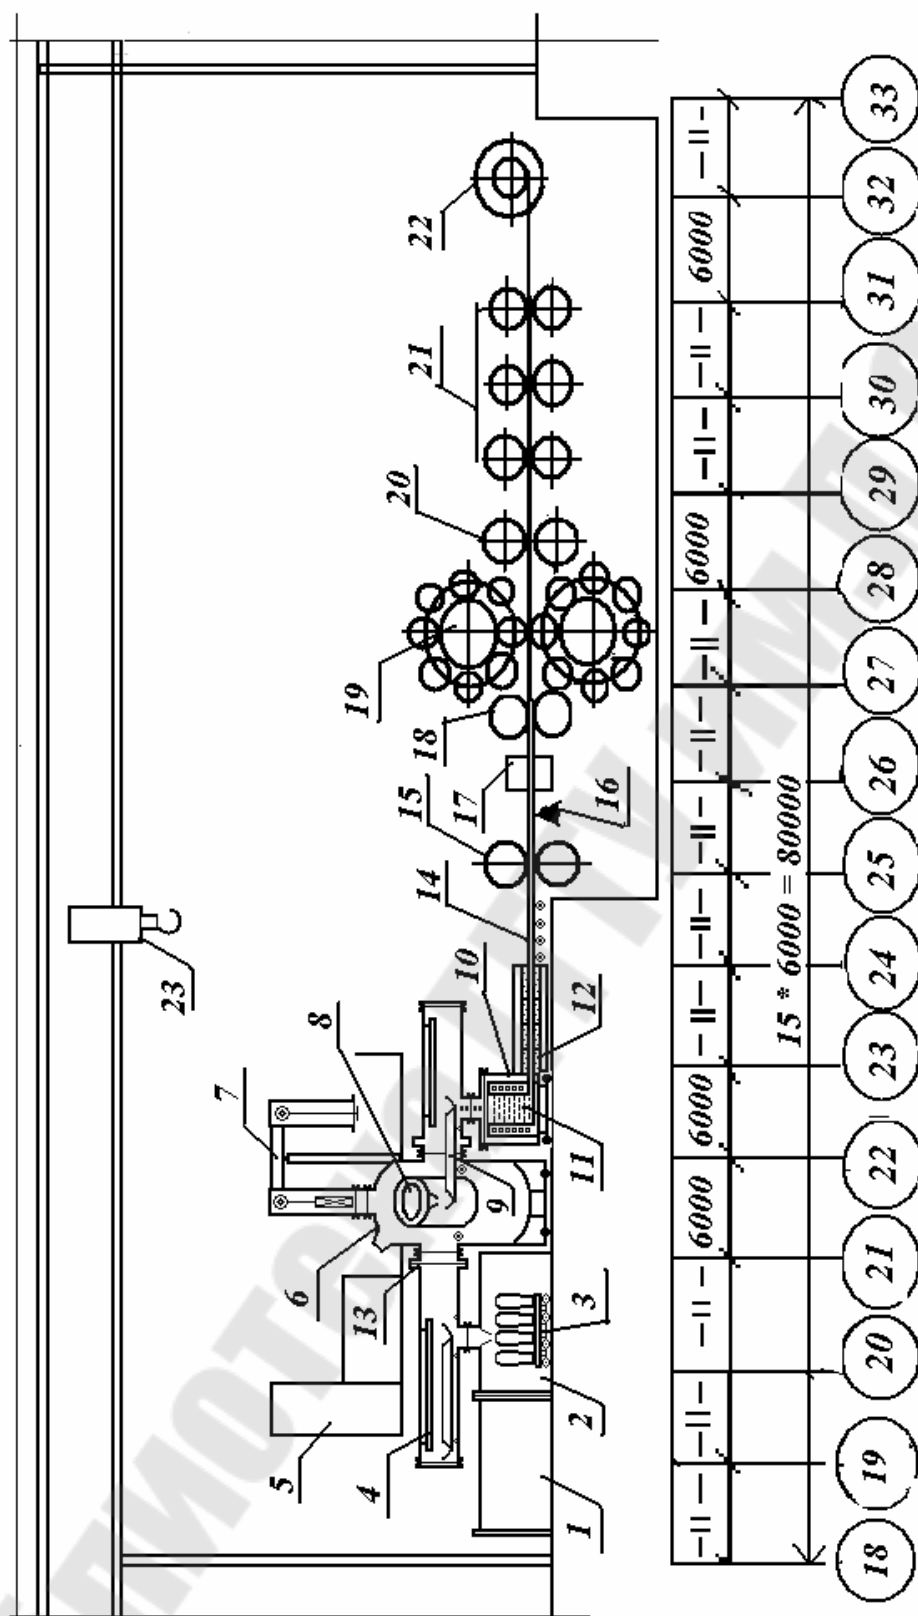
Схема разреза участка вакуумного литейно-прокатного агрегата с планетарным станом и МНГЛЗ. 1-вакуумная камера загрузки; 2-камера рзливки; 3-тележка с изложницами; 4-подогрев слитного жельоба; 5-блок управления; 6-печная вакуумная камера; 7-устройство загрузки печи; 8-индукционная плавильная печь; 9-разливочный желоб; 10-вакуумная камера; 11-индукционная печь подогрева МНГЛЗ; 12-кристаллизатор; 13-шиберный затвор; 14-литая непрерывная печь подогрева; 15-тянущие ролики; 16-ленточные ножницы; 17-индуктор; 18-задающая клетка; 19-планетарная клетка; 20-тянущие ролики; 21-клетки продольной прокатки; 22-моталка; 23-мостовой кран.
